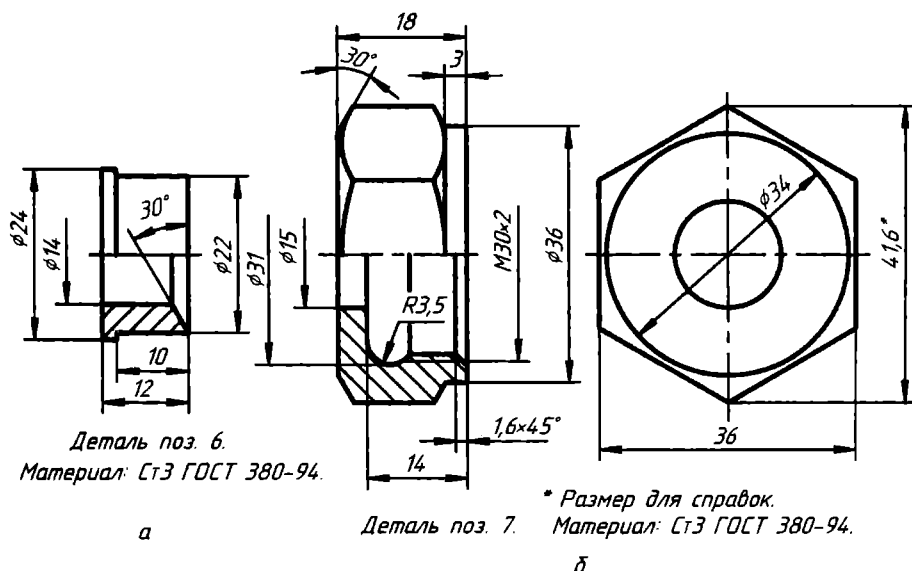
Чертежи: а — втулки; б — гайки нажимной
